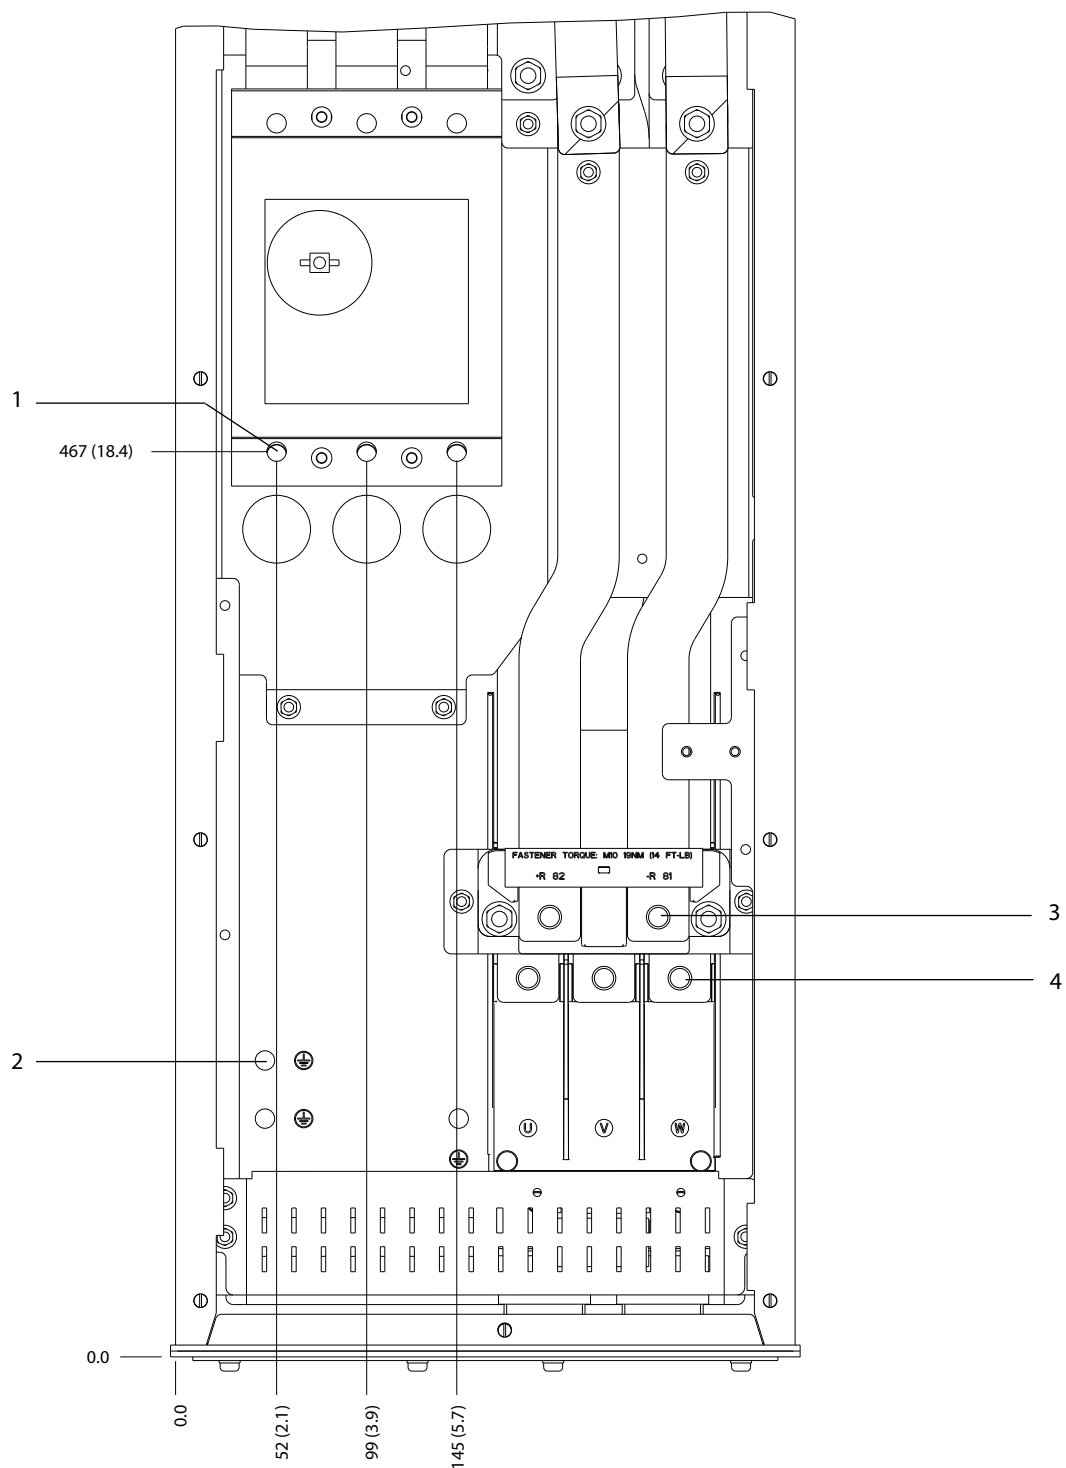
Dimensions des bornes D6h avec options contacteur et sectionneur (vue frontale)
